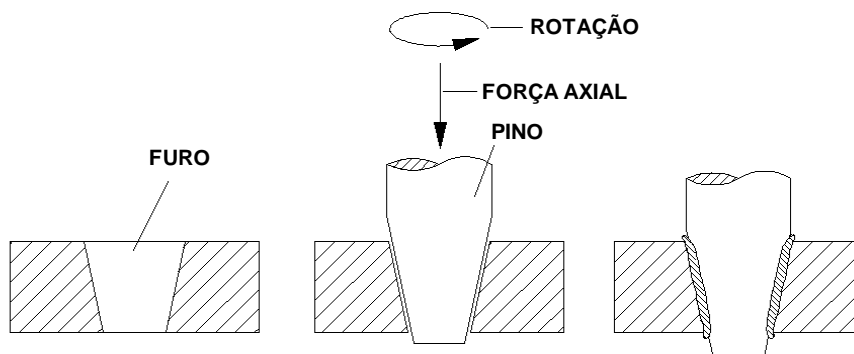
Ilustração das etapas do “*Tapered Plug Welding*”.
